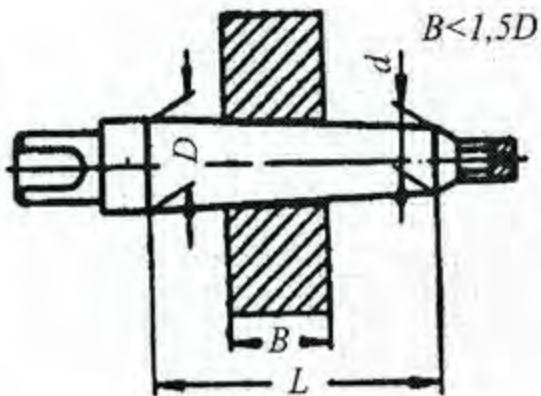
Установка заготовок на жорсткій конічній оправці
